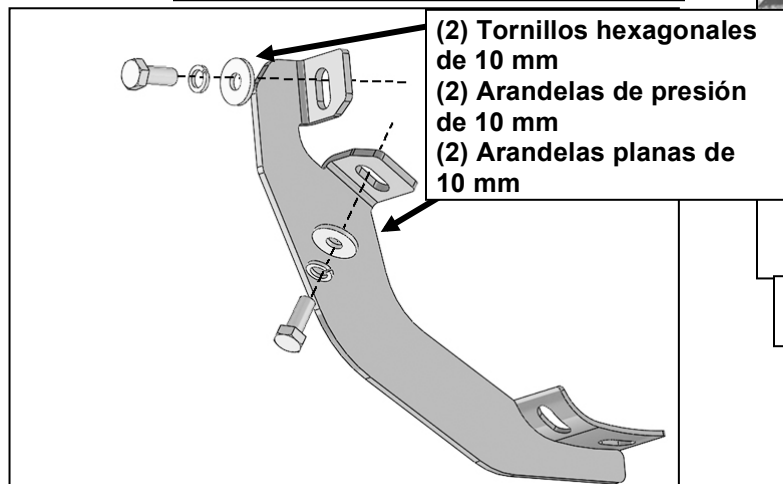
Atornillado del soporte de montaje frontal izquierdo/del lado del conductor
